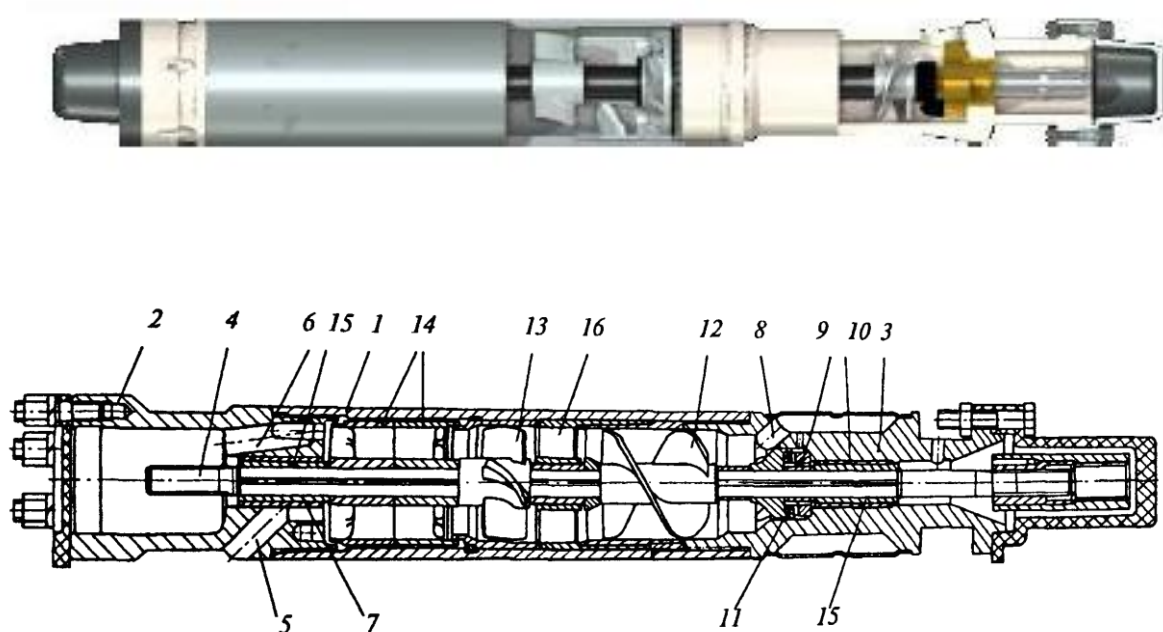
Газосепаратор: 1 – трубный корпус; 2 – головка; 3 – основание; 4 – вал; 5, 6 – перекрестные каналы; 7, 10, 15 – втулки радиальных подшипников; 8 – полость с каналами; 9 – подпятник; 11 – пята; 12 – шнек; 13 – рабочее колесо; 14 – сепараторы.
